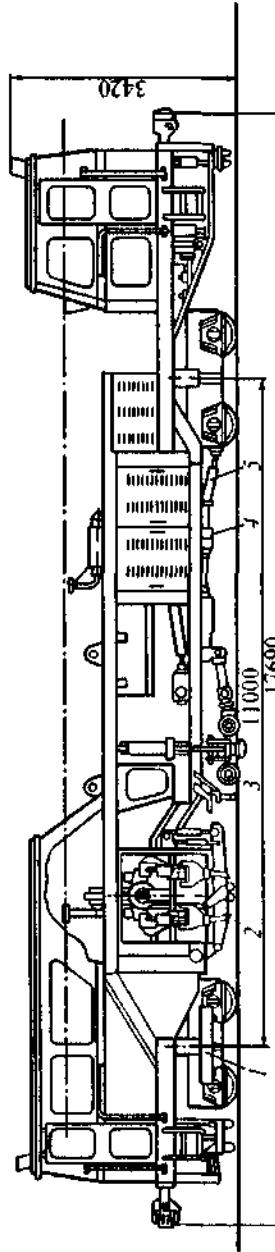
Машина выпрямочно-подбивочно-рихтовочная для стрелок и пути: 1 — уплотнитель балласта; 2 — блок подбивочный; 3 — механизм подъема и сдвигки пути; 4 — передача силыки пути; 5 — энергетическая установка
